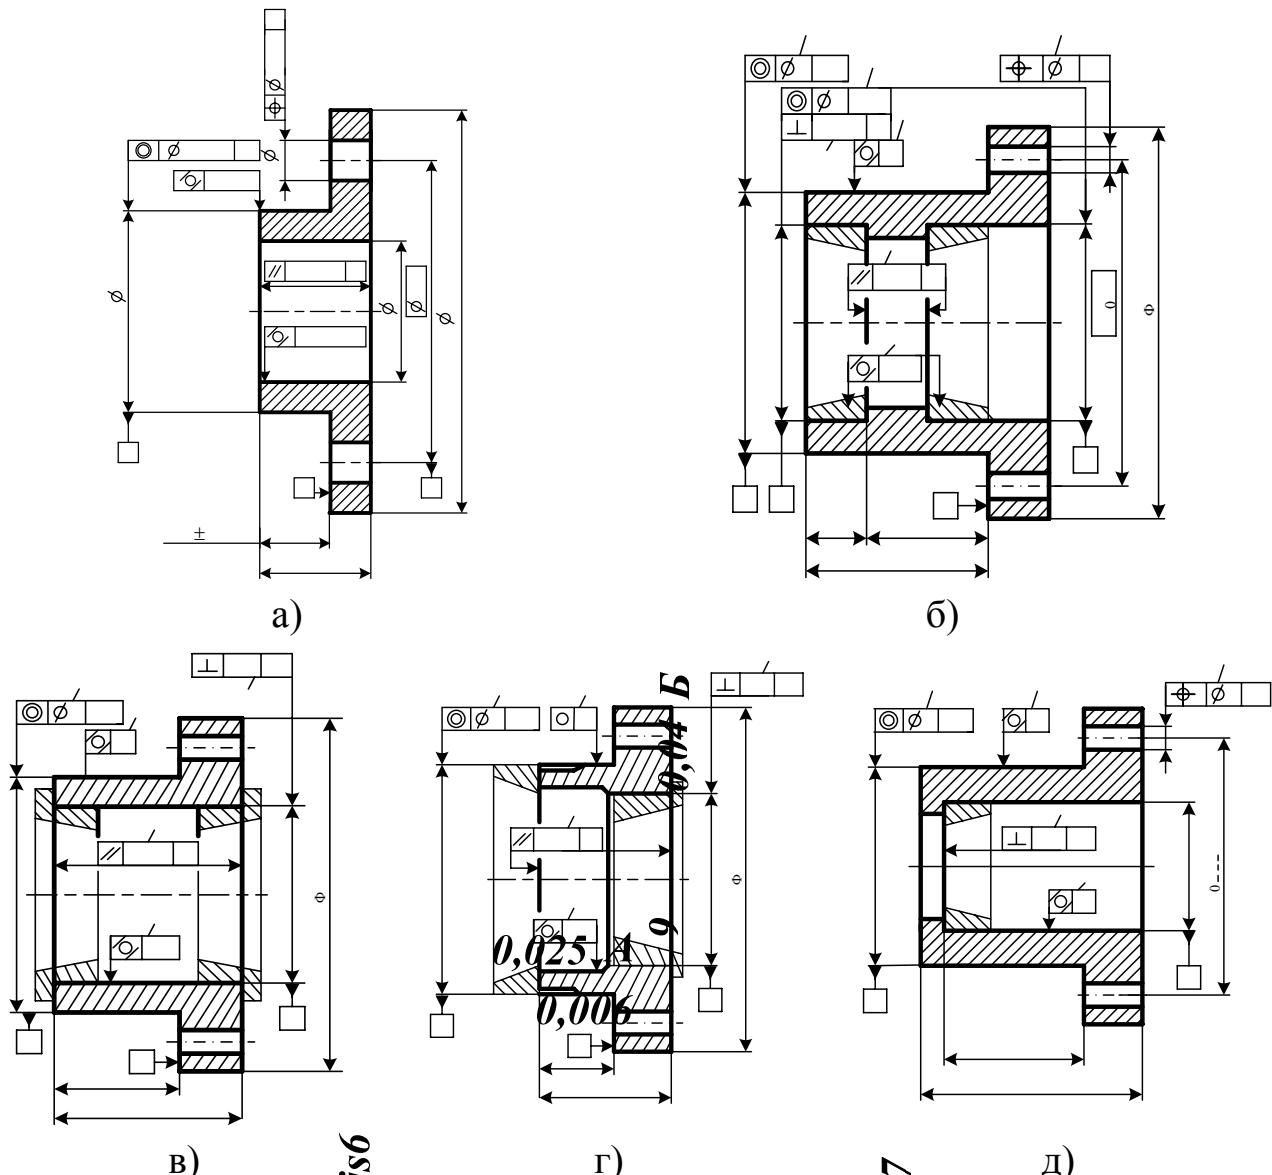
Позначення допусків форми і розташування поверхонь типових стаканів
